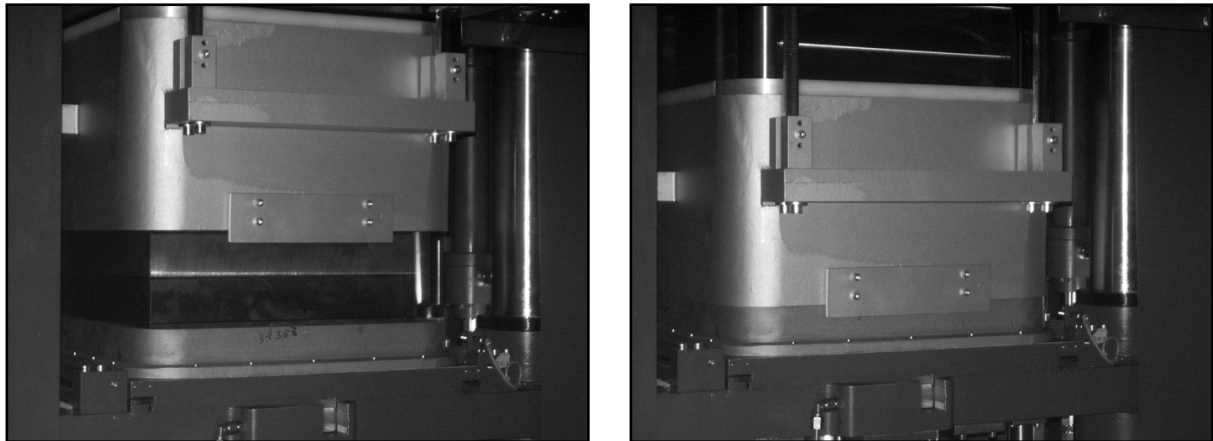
Geschlossenes Werkzeug ohne Einsatz der Vakuumkammer (links) und Pressverfahren unter Vakuum (rechts)
